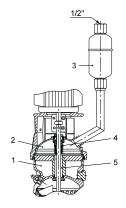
CR 1s, 1, 3 und 5 mit luftgekühlter Wellendichtungskammer
